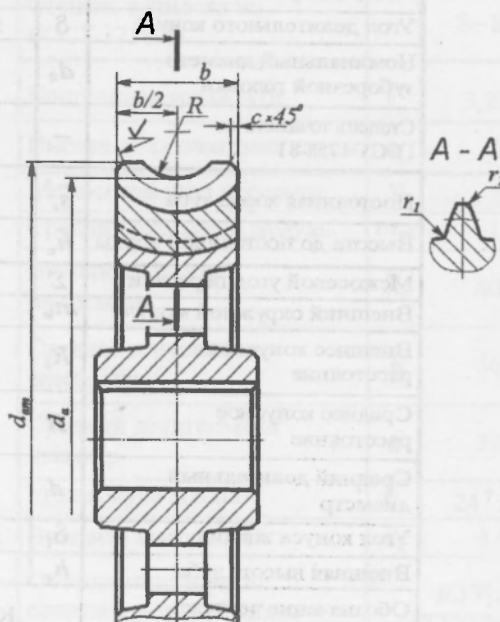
Обязательные параметры зубчатого венца червячного колеса
